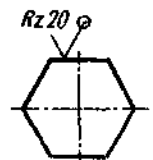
Нанесение обозначения шероховатости поверхностей контура
